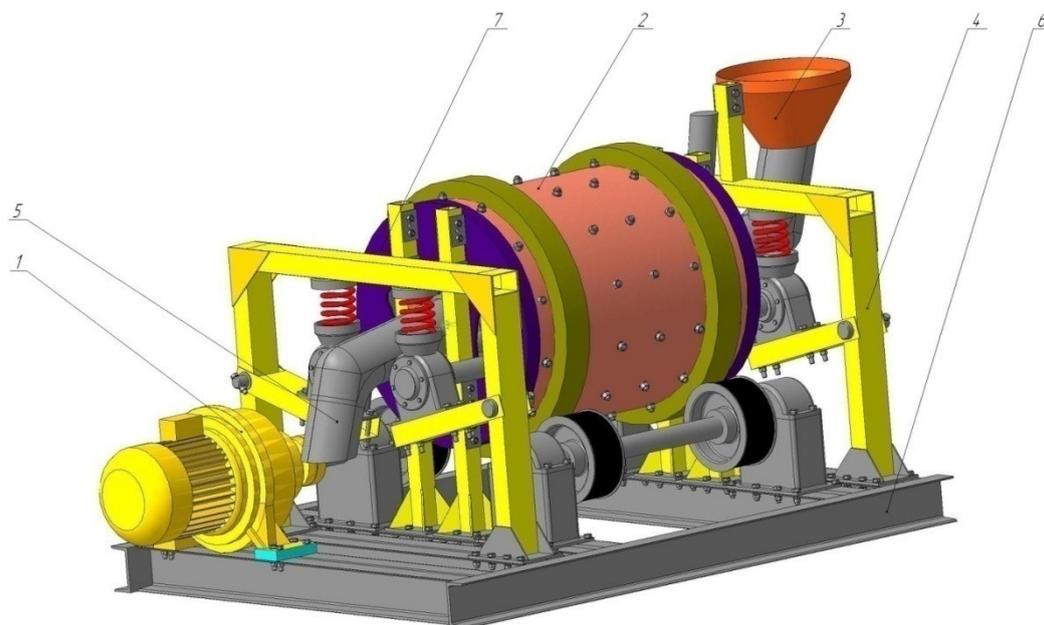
Валково-барабанная мельница: 1 – привод; 2 – обичайка; 3 – приемный бункер; 4 – механизм прижима(предохранительный механизм); 5 – выгрузочная труба; 6 – рама
